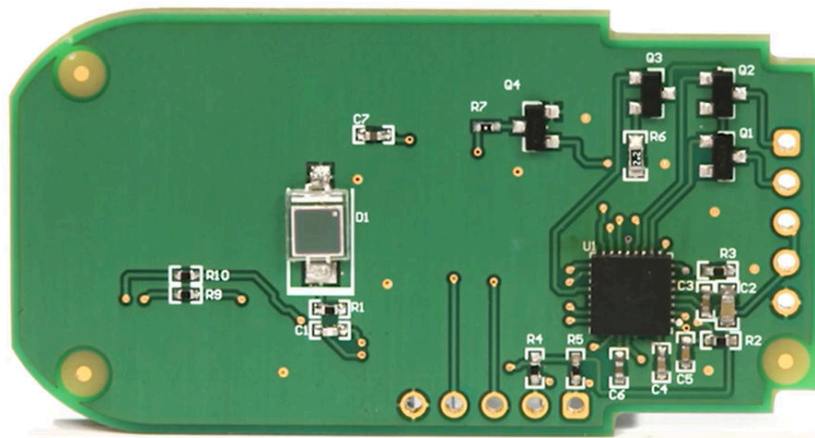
脉搏血氧仪的 TIDA-010267 PCB
